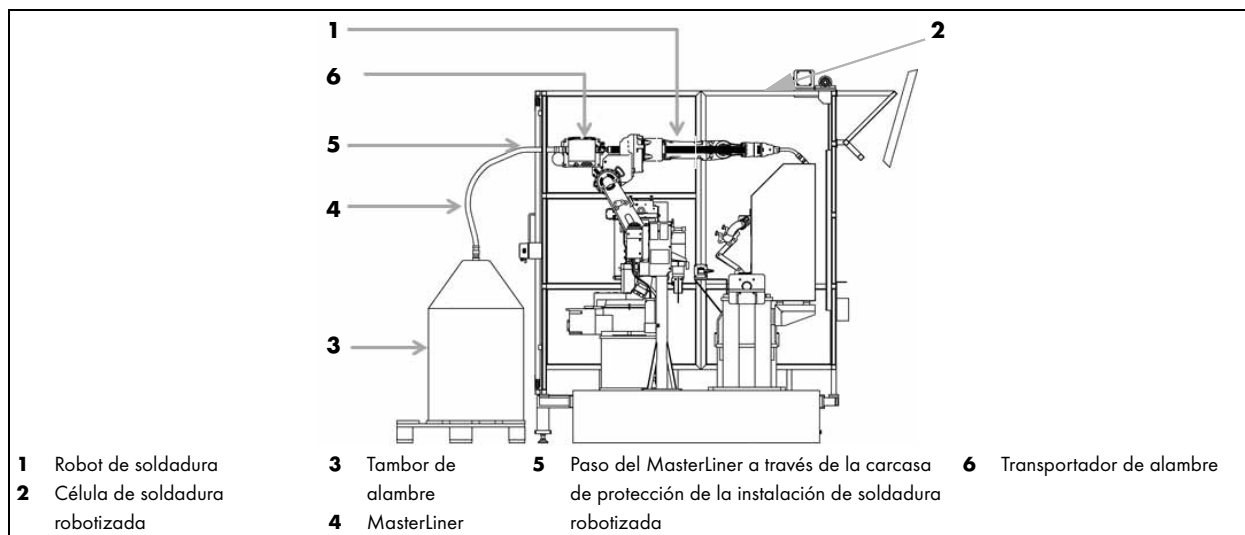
Tendido de la célula de soldadura robotizada
